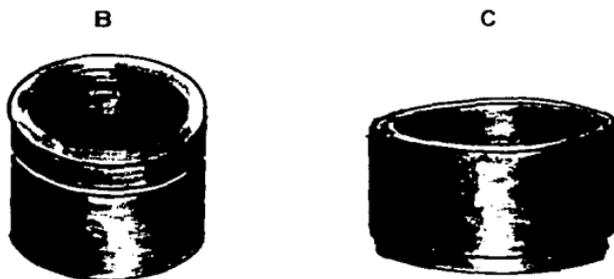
B POSICION DEL MOLDE PARA EL MATERIAL DE IMPRESION DEL BLOQUE TESTIGO.
